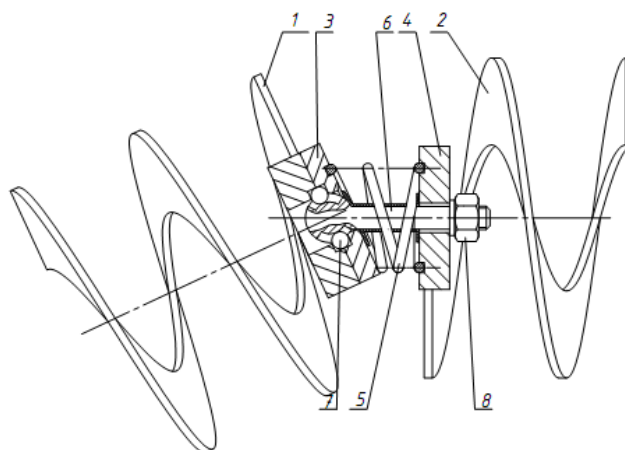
Конструктивна схема гвинтового секційного робочого органу конвеєра [288]: 1, 2 – спіралі; 3 і 4 – оправки; 5 – пружина; 6 – шарнірне болтове з'єднання; 7 – кулька; 8 – гайка
